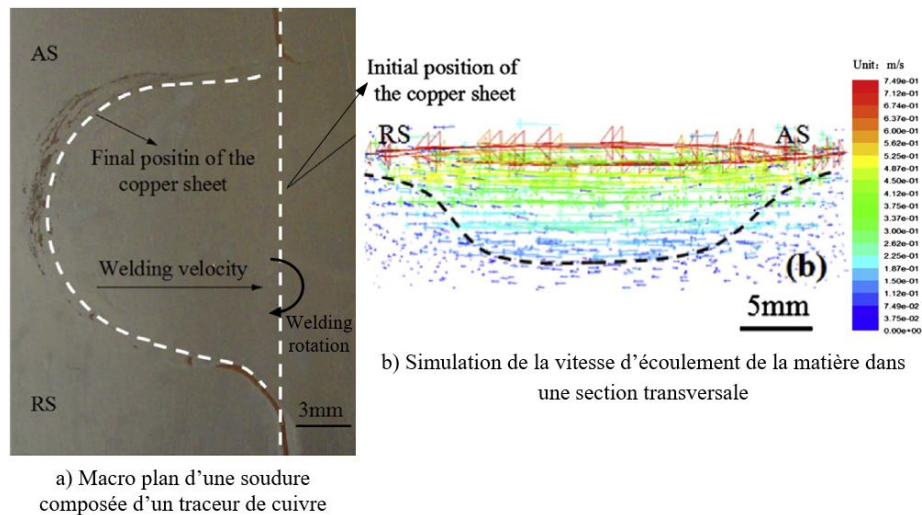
Étude de l'écoulement d'une soudure en AA6061-T6 [29]
